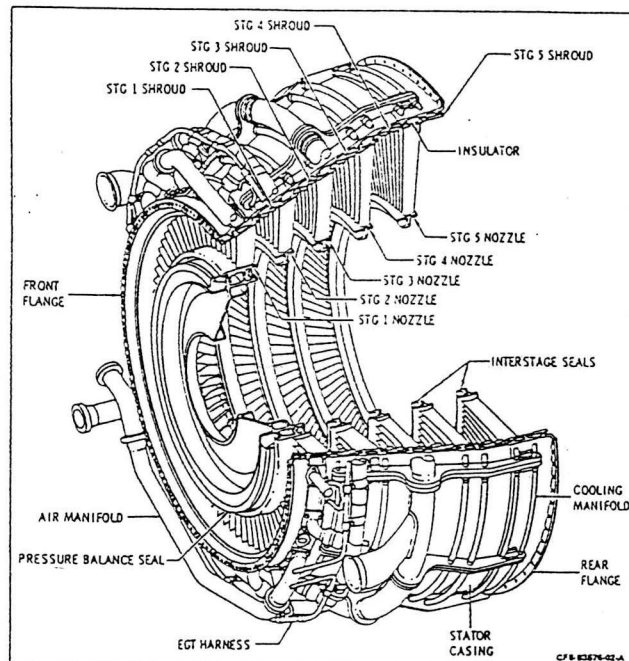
แสดงภาพ E Module (High Pressure Turbine Assembly)
